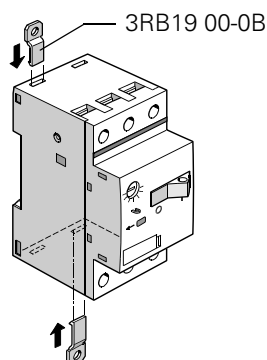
Schraubbefestigung der 3RV1 (Beispiel: Baugröße S00)
